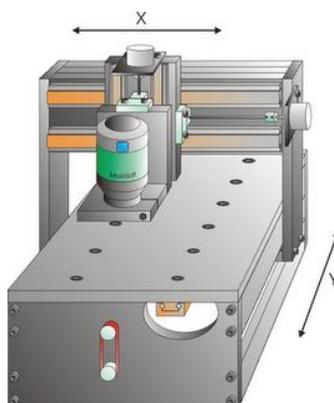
Станок ЧПУ с движущимся порталом
